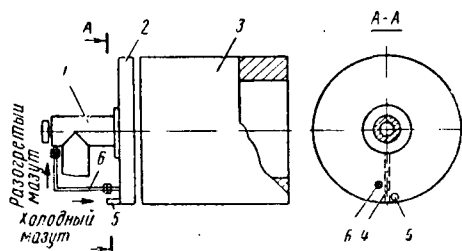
Устройство для разогрева мазута: 1 — форсунка топливная; 2 — полое кольцо; 3 — топка; 4 — перегородка; 5, 6 — трубки
